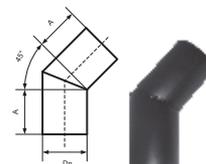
Отвод 45° сварной 2-х сегментный
